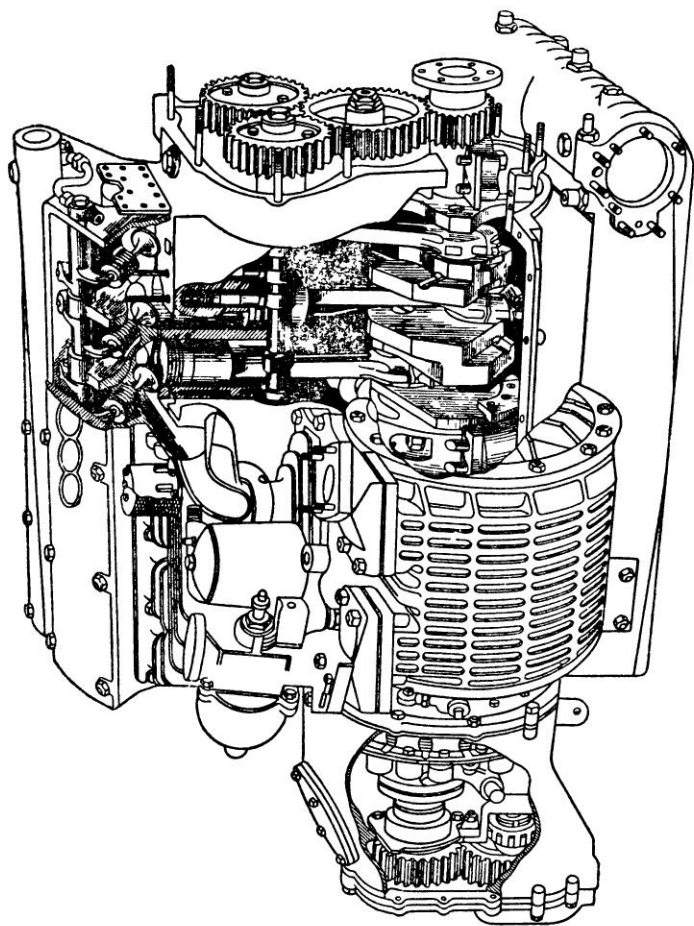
Привод верхних распределительных валов цилиндрическими шестернями
